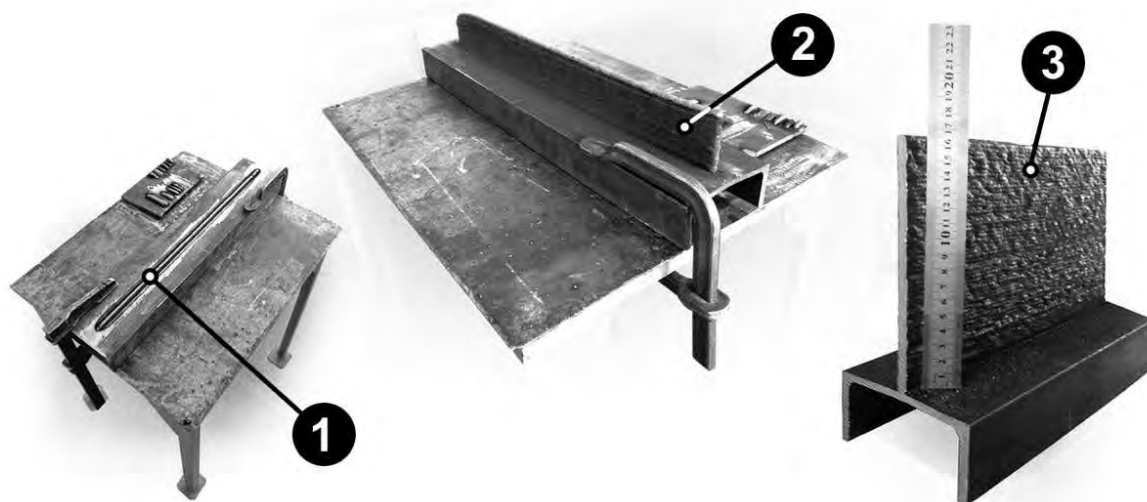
Внешний вид и стадии аддитивной наплавки: 1 – первый слой наплавки; 2 – внешний вид после наплавки 16 слоев; 3 – внешний вид после наплавки 55 слоев
